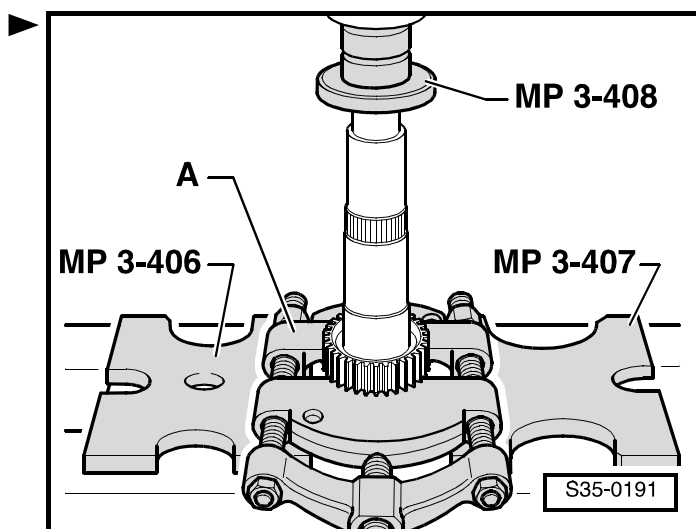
Извлечение внутреннего кольца конического роликоподшипника
